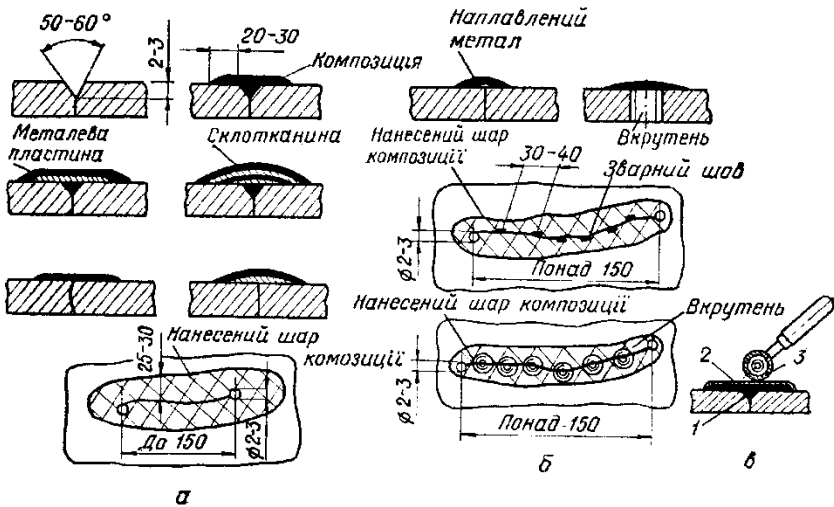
Заклеювання тріщин: а – коротких; б – довгих; в – прикочування накладки роликком; 1 – накладка; 2 – шар епоксидної суміші; 3 – ролик
